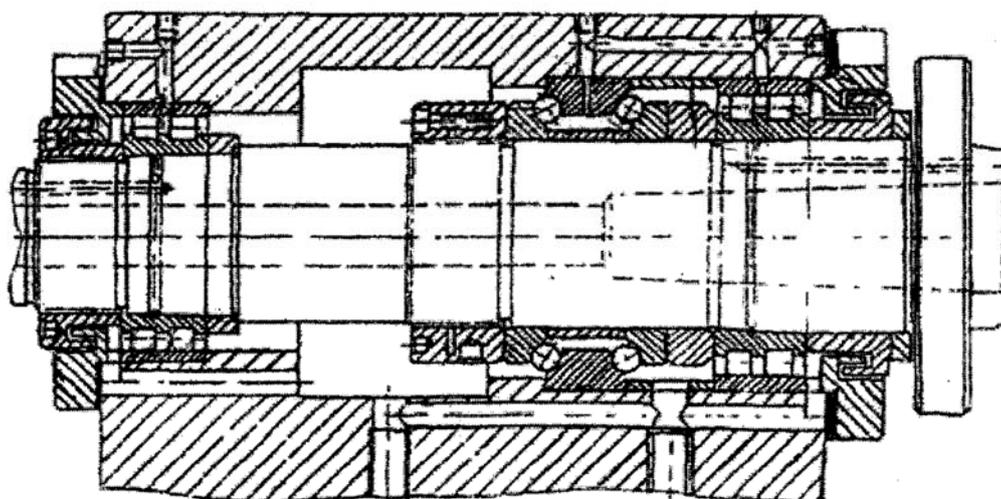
Шпиндельный узел станка с ЧПУ на роликоподшипниках типа 3182100 в обеих опорах и на шариковом упорно-радиальном типа 178000 в передней опоре
